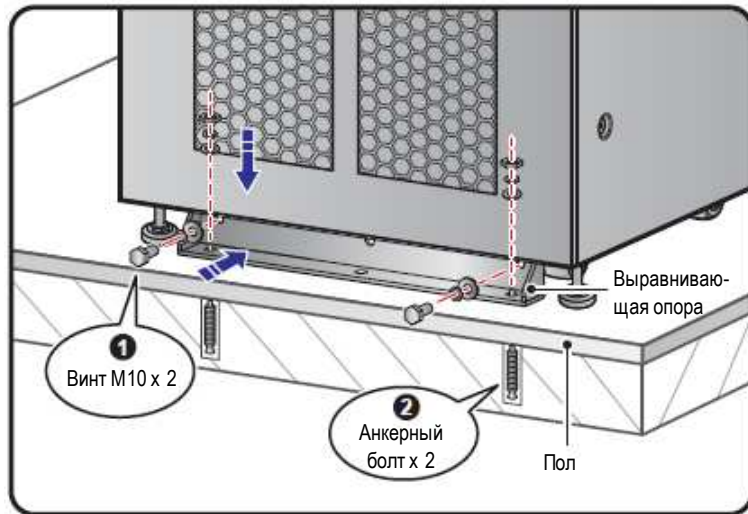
Установка задней выравнивающей опоры ИБП
